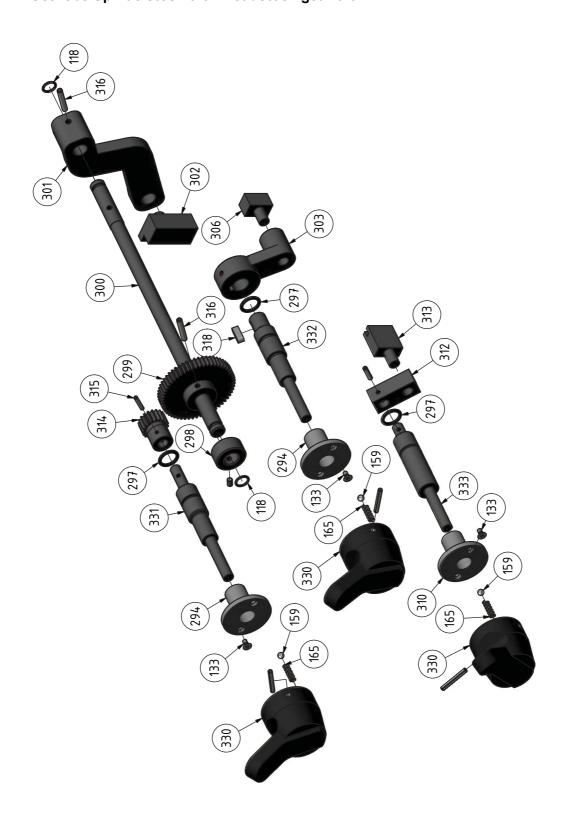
Getriebe Spindelstock 6-6 - Headstock gear 6-6
